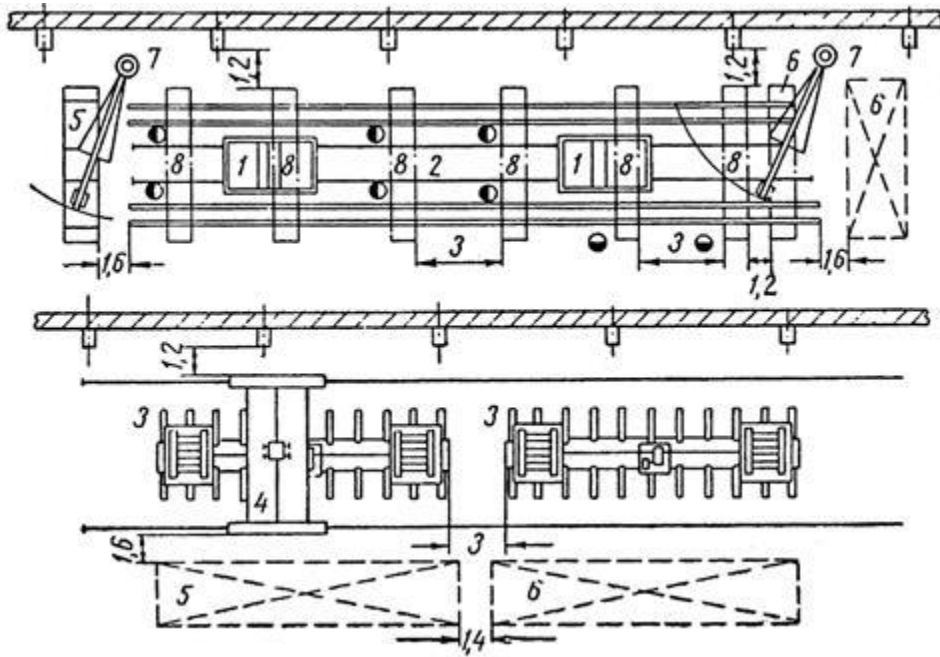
Схеми розташування установок для механізованого збирання і автоматичного зварювання під флюсом балок та інших металевих конструкцій:
